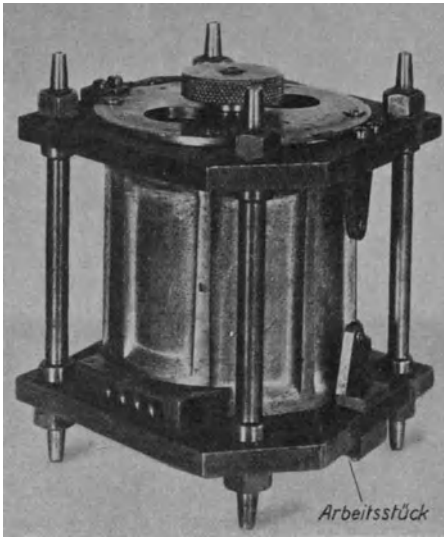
Vorrichtung zum Bohren des Mantels für die elektrische Handbohrmaschine.
